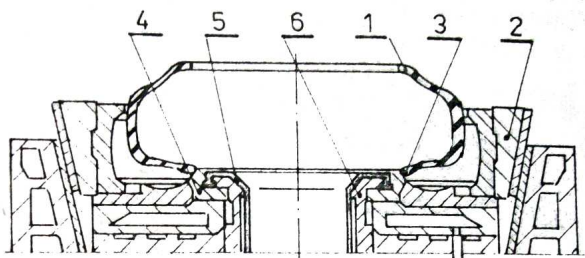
Vulkanizační lis Bag-o-matic s půlenou formou
